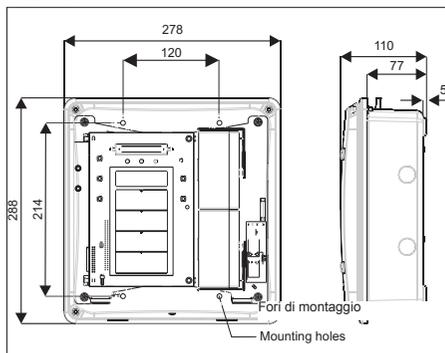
Dimensioni del Gasmaster con i fori di montaggio
